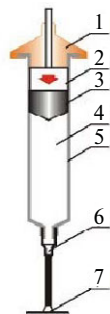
Схема нанесения припойной пасты на контактные площадки с помощью диспенсера: 1 – крышка; 2 – воздух под давлением; 3 – поршень; 4 – припойная паста; 5 – цилиндрический корпус; 6 – сопло; 7 – контактная площадка
